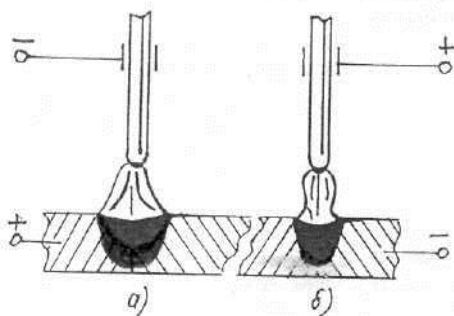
Форма зварювальної дуги при прямій (а) та зворотній (б) полярності
